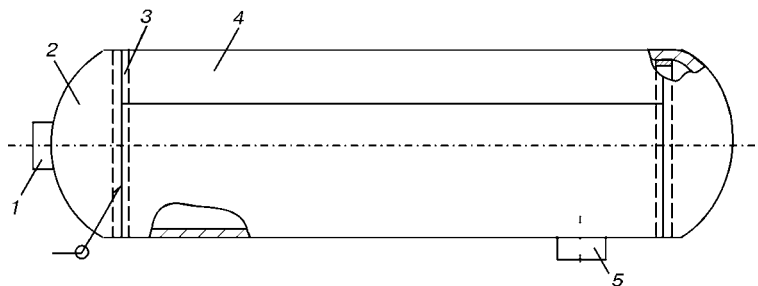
Схема разделения резервуара на конструктивные элементы: 1, 5 — штуцера; 2 — днище; 3 — кольцо подкладное; 4 — обечайка
